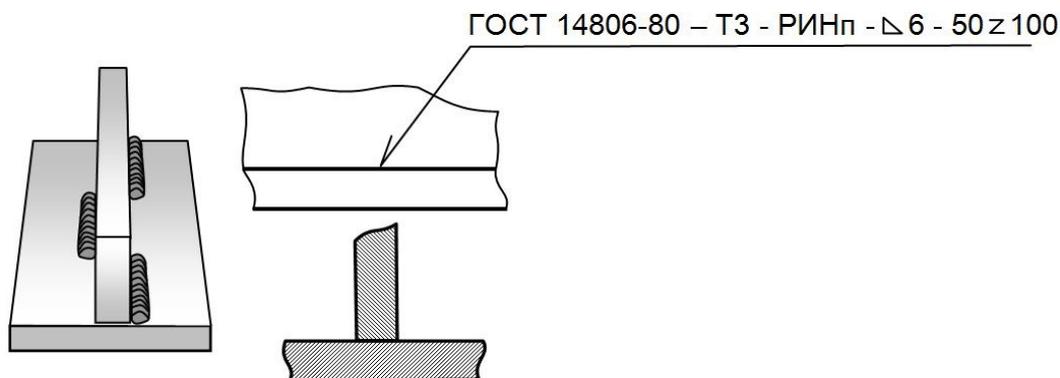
Условное обозначение сварного шва вида Т
